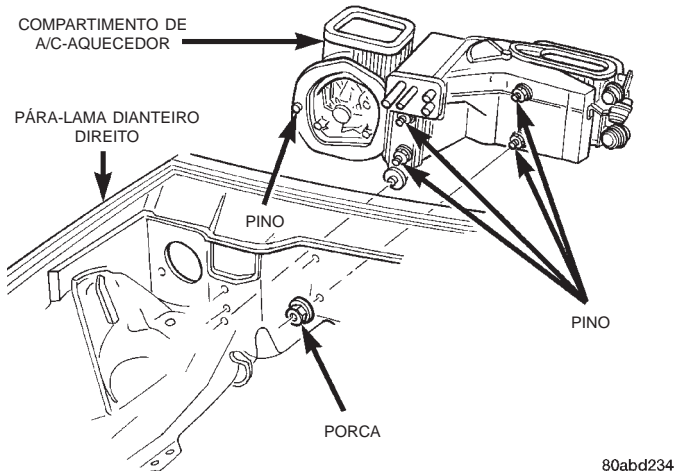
Remoção/Instalação do Compartimento de A/C-Aquecedor
